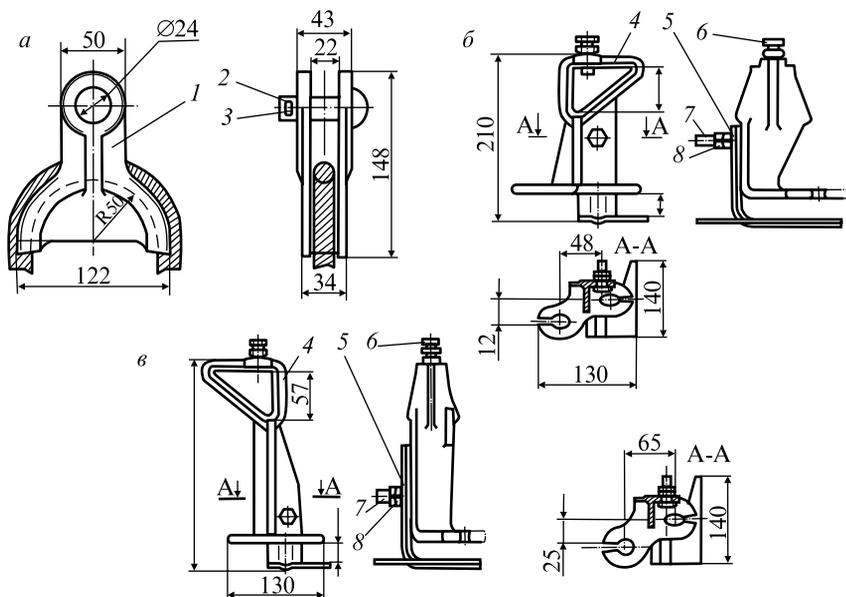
Арматура из чугуна: *а* — коуш вилочный под серьгу 006; *б* и *в* — стойки сочлененного прямого и обратного фиксаторов; *1* — коуш вилочный; *2* — валик; *3* — шплинт; *4* — стойка фиксатора; *5* — отбойник; *6, 7* — болт М12; *8* — гайка М12
